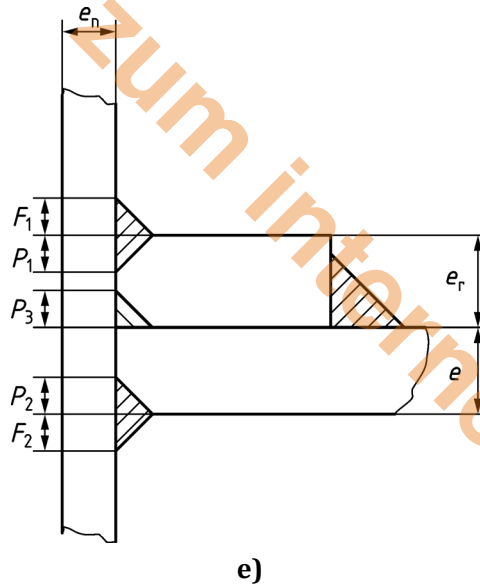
Typische Ausführungen von eingeschweißten Anbauteilen
